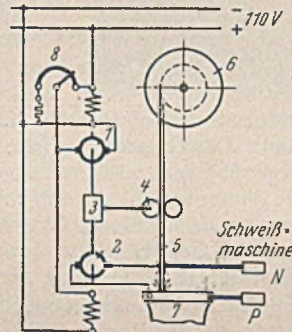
Schaltbild einer selbsttätigen Kohlelichtbogenschweißeinrichtung der Siemens-Schuckertwerke AG.
